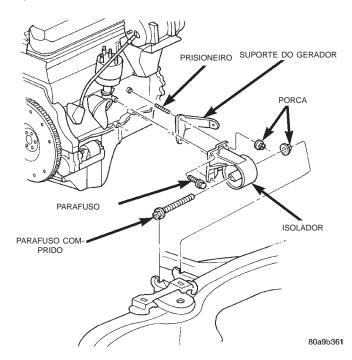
Conjunto Dianteiro Direito de Montagem do Motor
